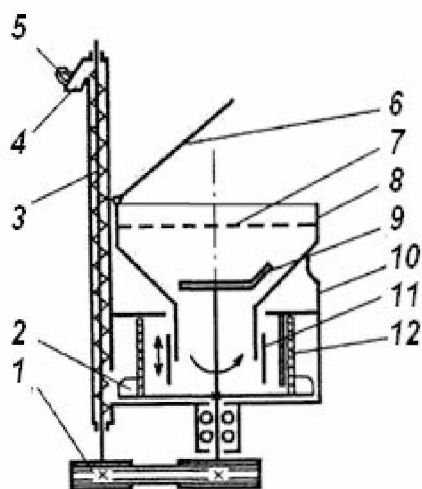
Схема просіювача А2-ХПВ: 1 – привід з клинопасовою передачею; 2 – подавальні лопаті; 3 – вивантажувальний шнек; 4 – вивантажувальний патрубок; 5 – магнітний уловлювач; 6 – кришка бункера; 7 – запобіжна решітка; 8 – приймальний бункер; 9 – зворушувач; 10 – корпус; 11 – телескопічний патрубок; 12 – циліндричний ситовий барабан
